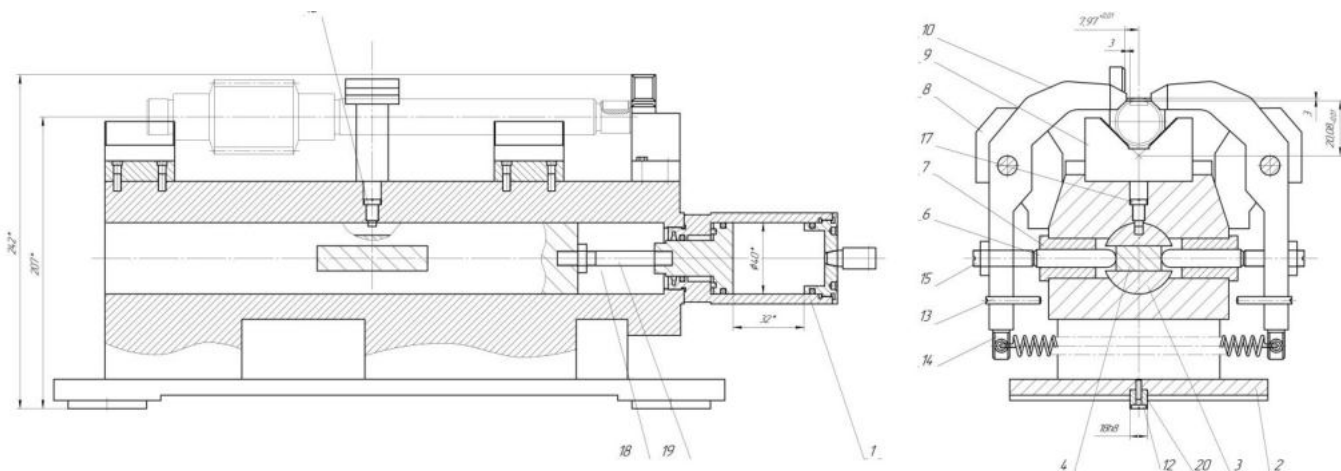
Пристосування для фрезерування шпоночного пазу
